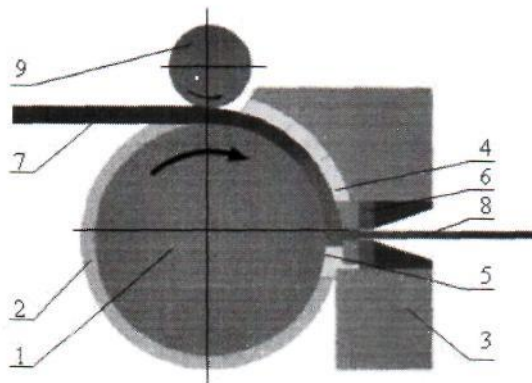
Схема процесу безперервного пресування за способом Конформ:
